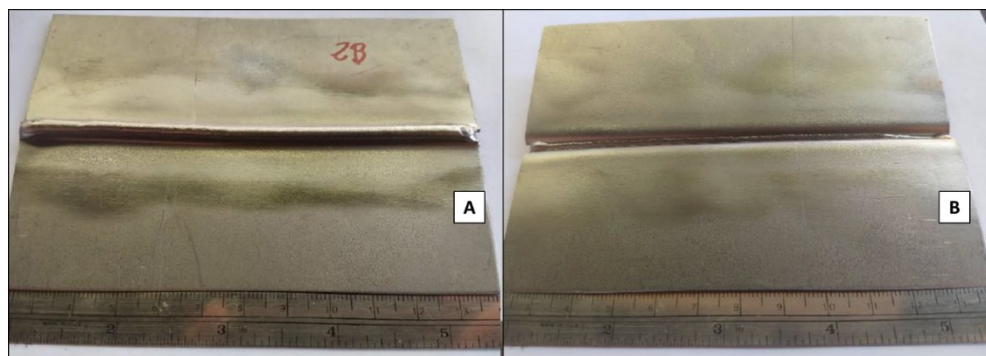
Condição 2 de soldagem GMAW. A) vista de cima da chapa soldada B) Vista do verso da solda (Próprio autor)
